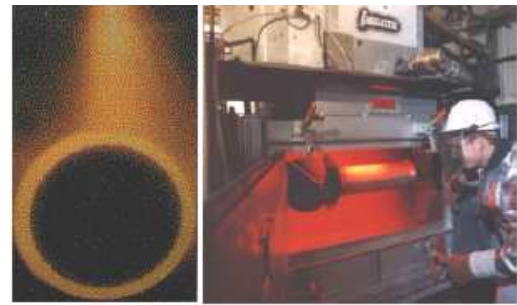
Спрейне лиття трубчастої заготовки (а) і деталі складної форми (б)
